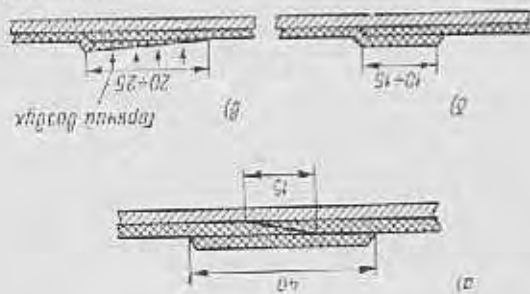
Типы сварных соединений полиизобутилена
